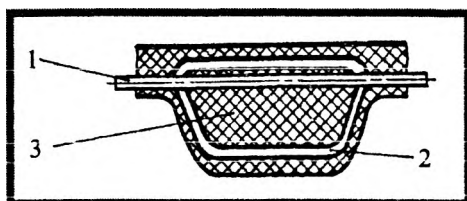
Зубчатый ремень с поперечными профильными пружинами:
